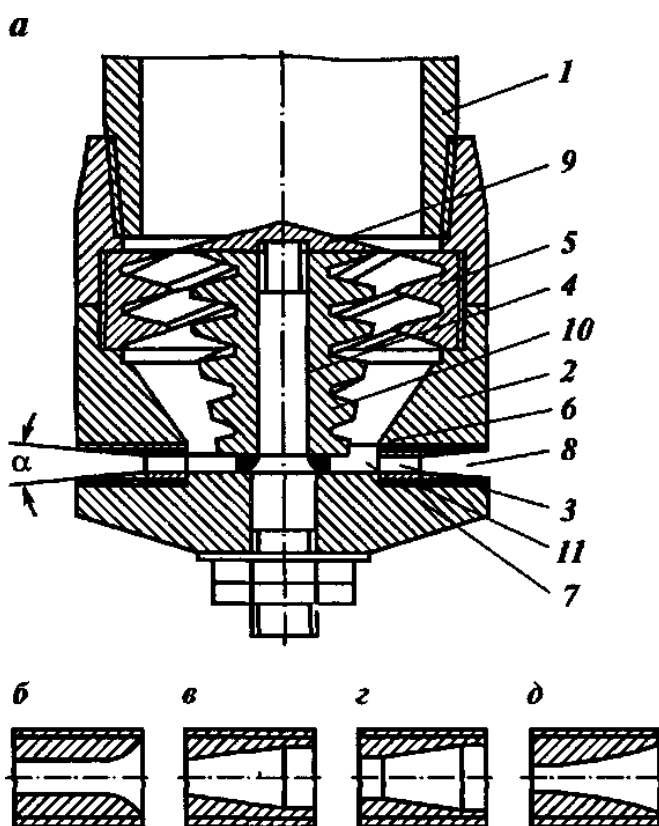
Схема устройства двухкаскадного пульсатора с насадками
